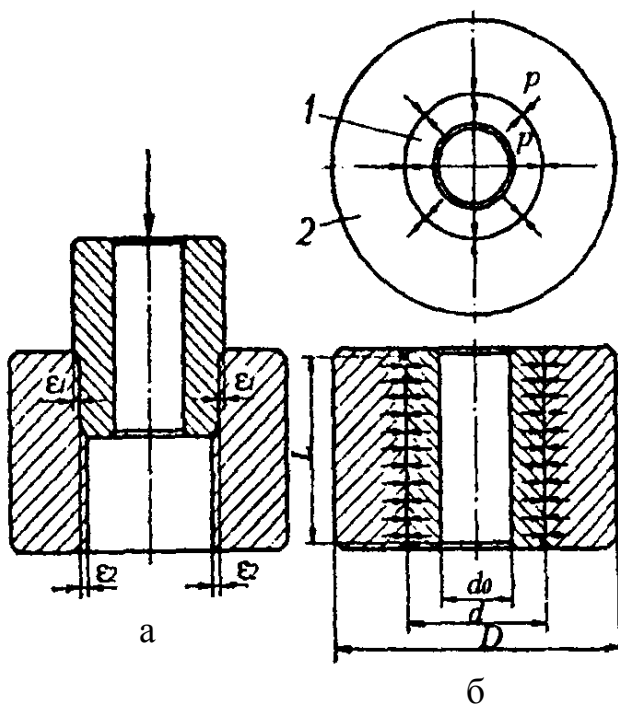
Схема запресовування (а) і схема пресового з'єднання (б): 1 – натяг охоплюваної деталі; 2 – натяг охопленої деталі.
